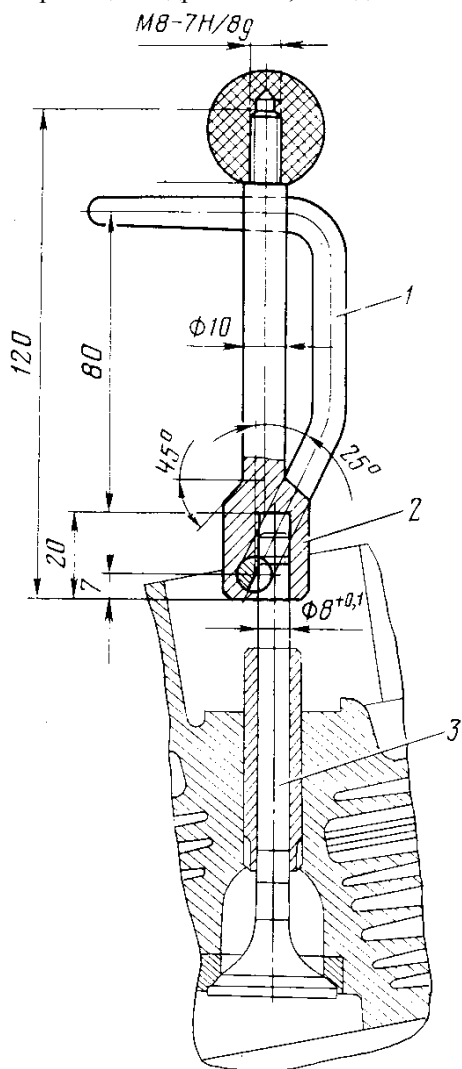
Приспособление для притирки клапанов: 1 — зажим; 2 — оправка; 3 — клапан.
